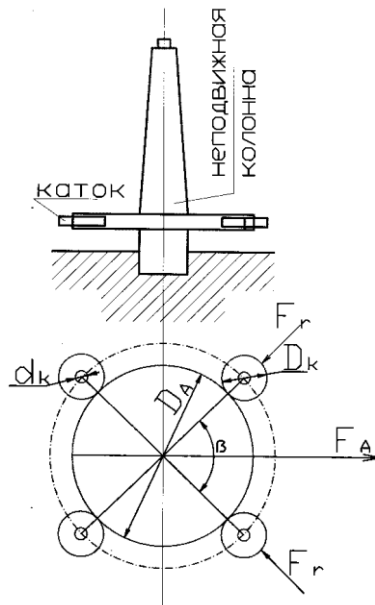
Расчетная схема опорных нагрузок на катки крана с неподвижной колонной
